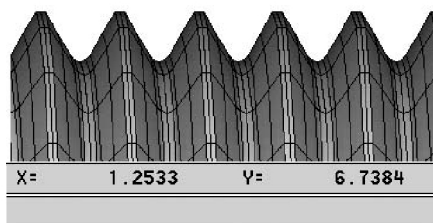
Фрагмент инструмента для создания внутренней резьбы
